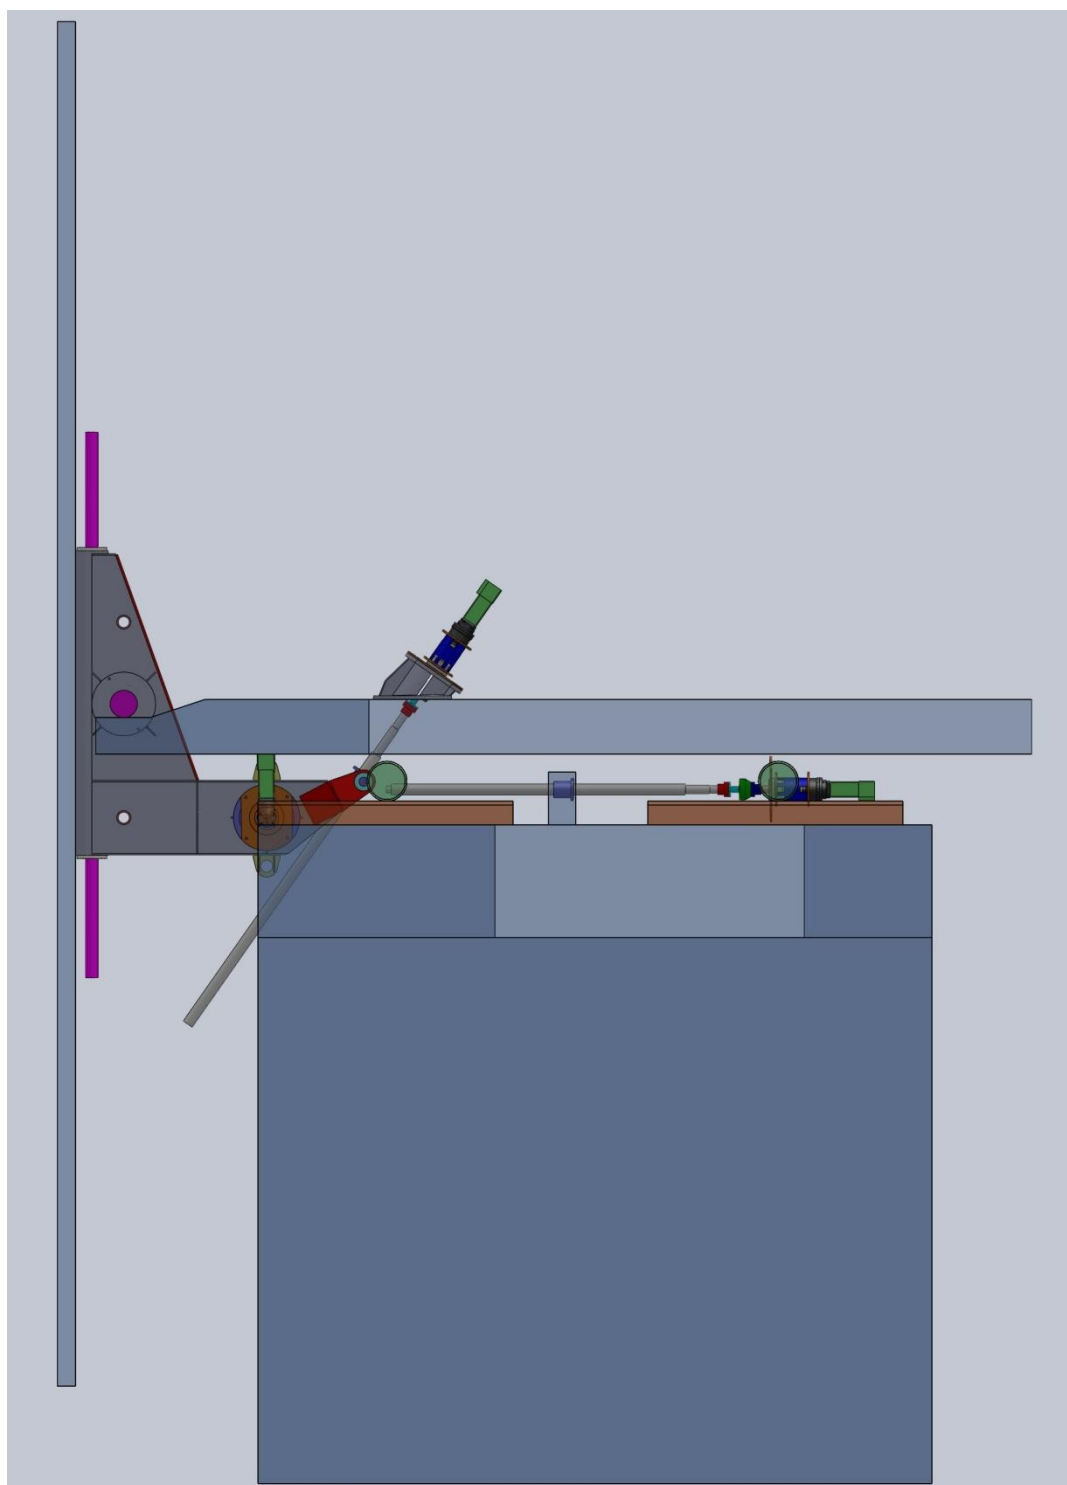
Новый угломестный привод с ШРУСом (сборка)
